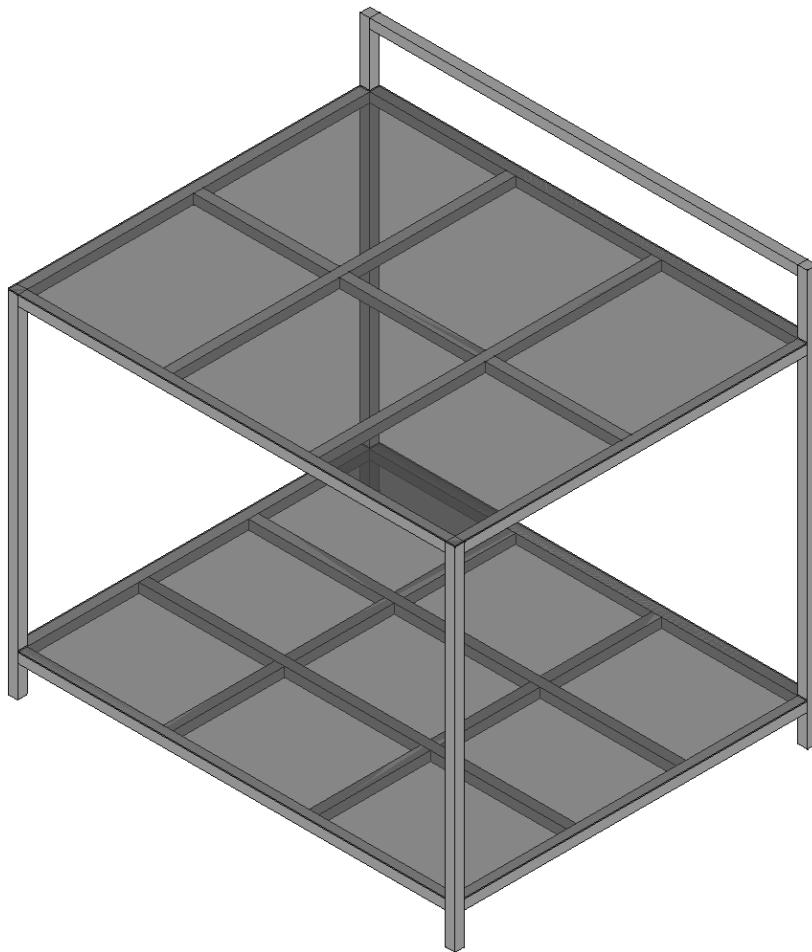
Representación gráfica de la estructura metálica donde se dispondrá la batería de flujo redox. Fuente: Elaboración propia.
